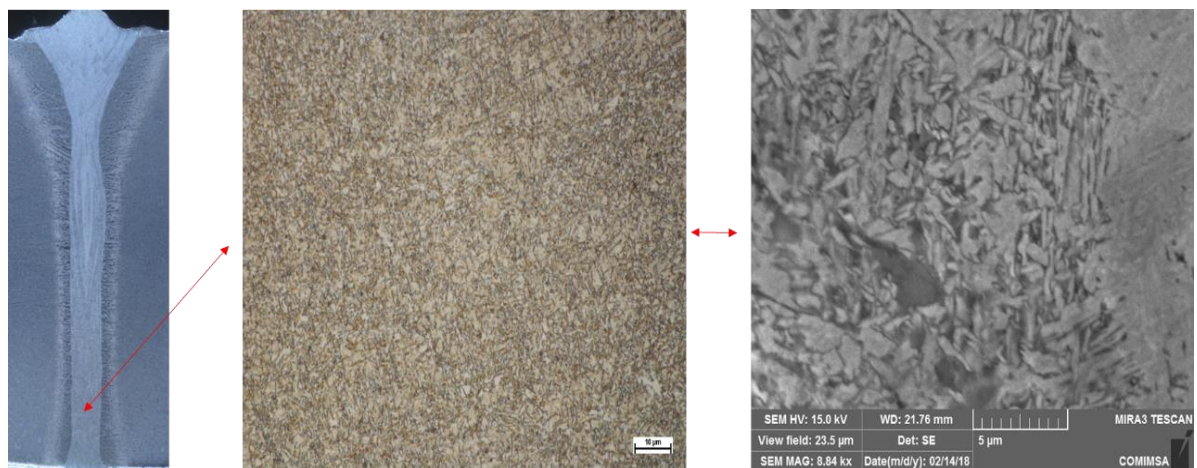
vista microscópica de la parte inferior de la soldadura.
